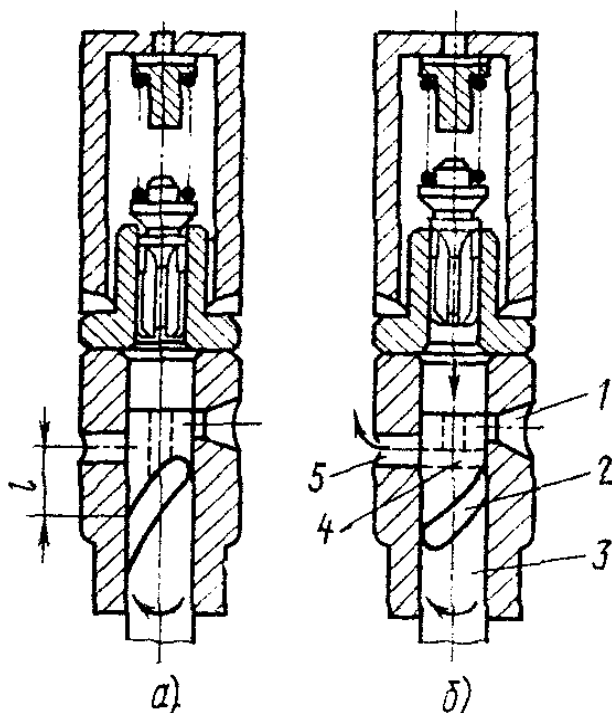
Схема регулювання подачі палива поворотом плунжера:
